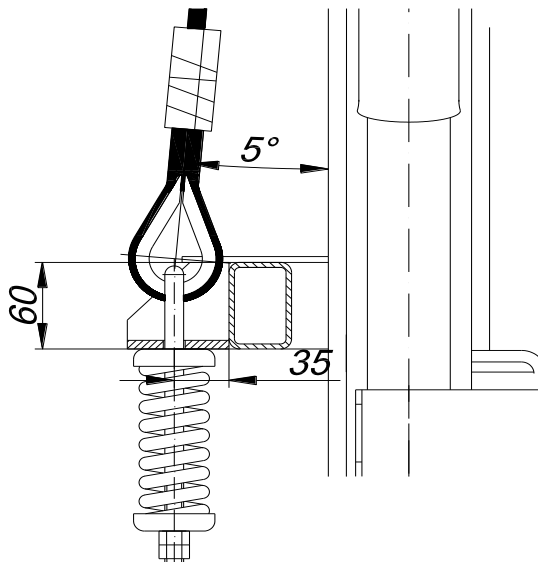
Схема до розрахунку зварного з'єднання упору до рами підвіски
